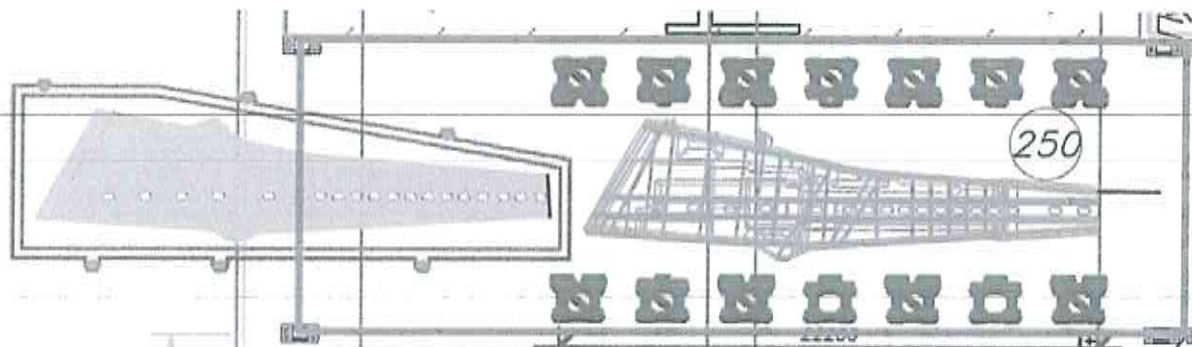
Место установки обрабатывающего 5-координатного центра с ЧПУ
